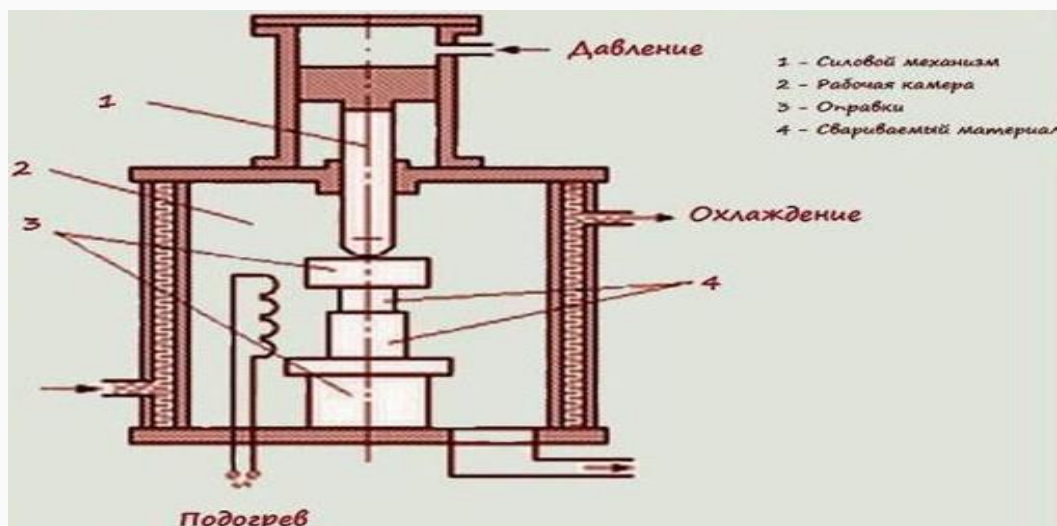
Типовая схема установки для диффузионной сварки:
